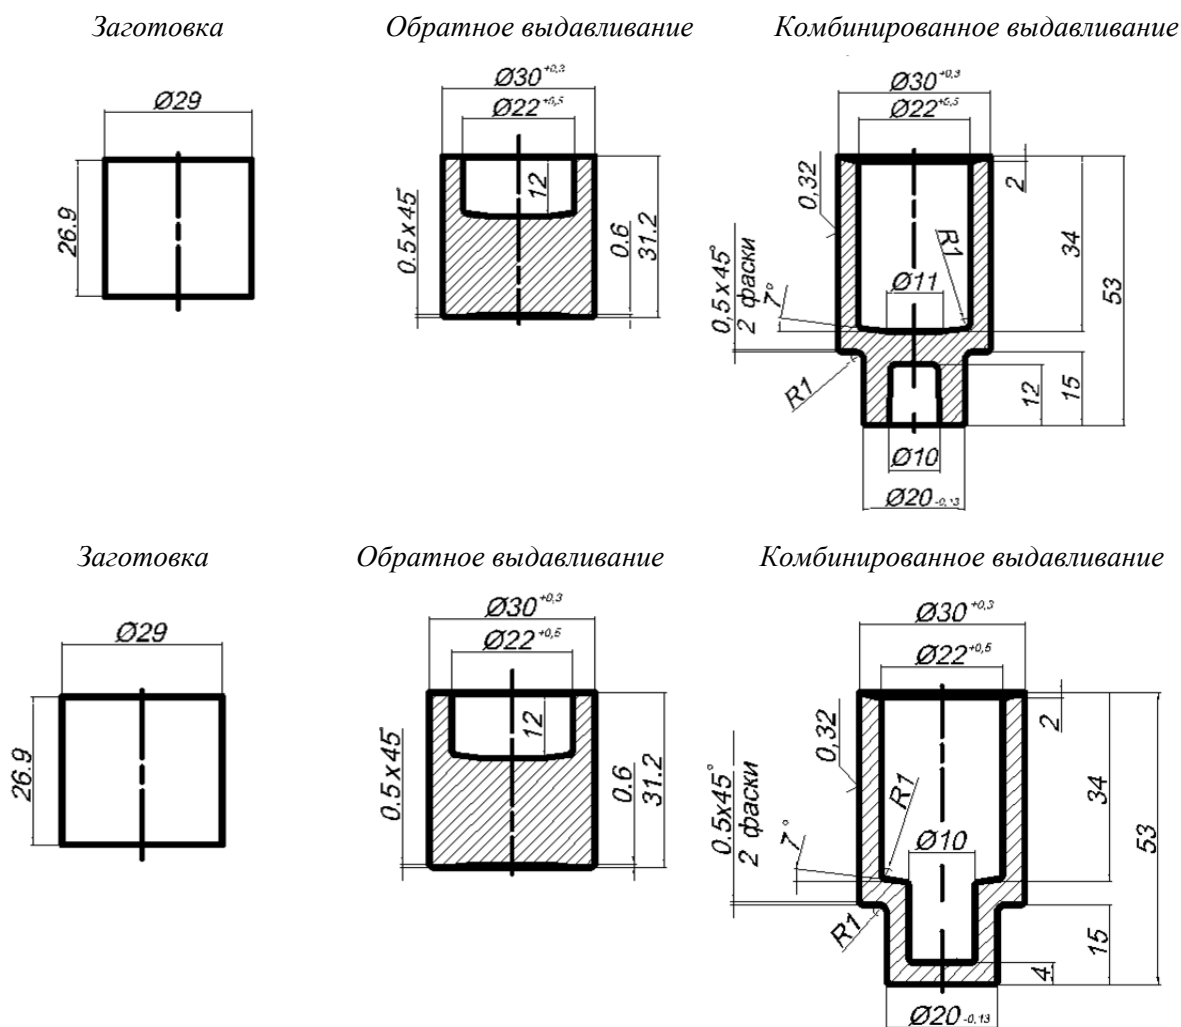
Технологические переходы изготовления детали «поршень тормозного цилиндра»
